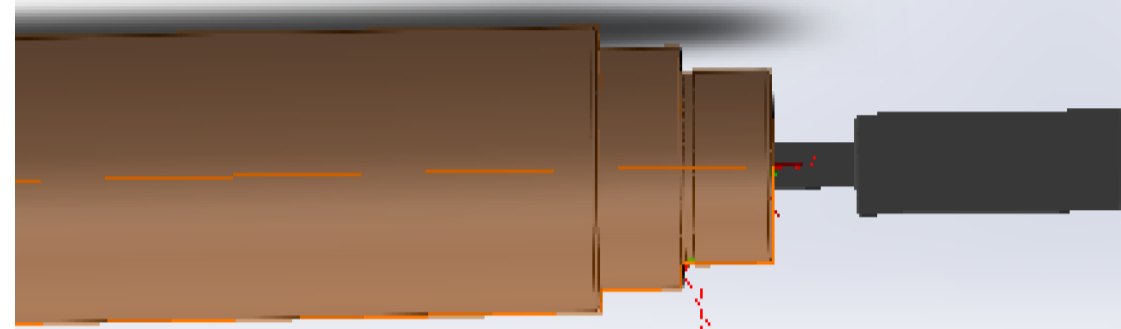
Точіння канавки $\varnothing 34,5$
